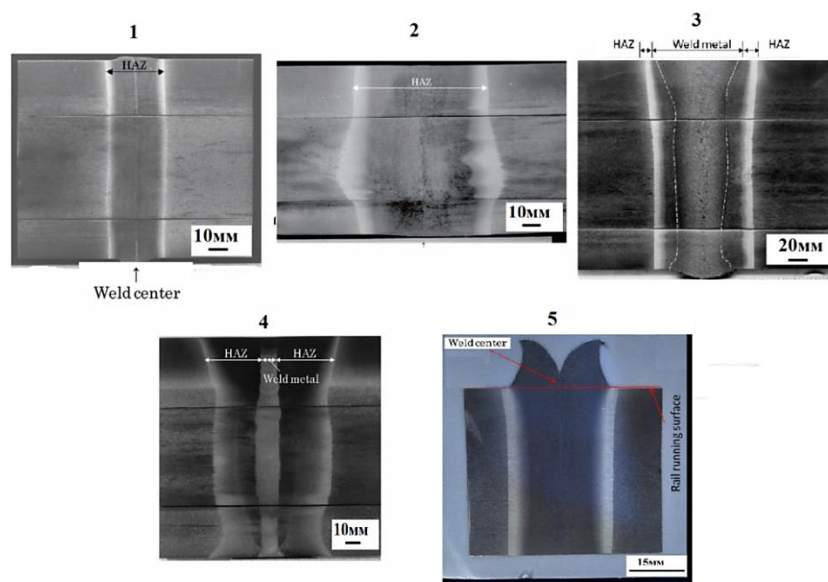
Макроструктуры, зоны сварки и ЗТВ в зоне сварного стыка рельса, сваренного разными способами: 1 – контактно-стыковая сварка оплавлением; 2 – газопрессовая сварка; 3 – алюминотермитная сварка; 4 – сварка закрытой дугой (Enclosed arc welding); 5 – линейная сварка трением
